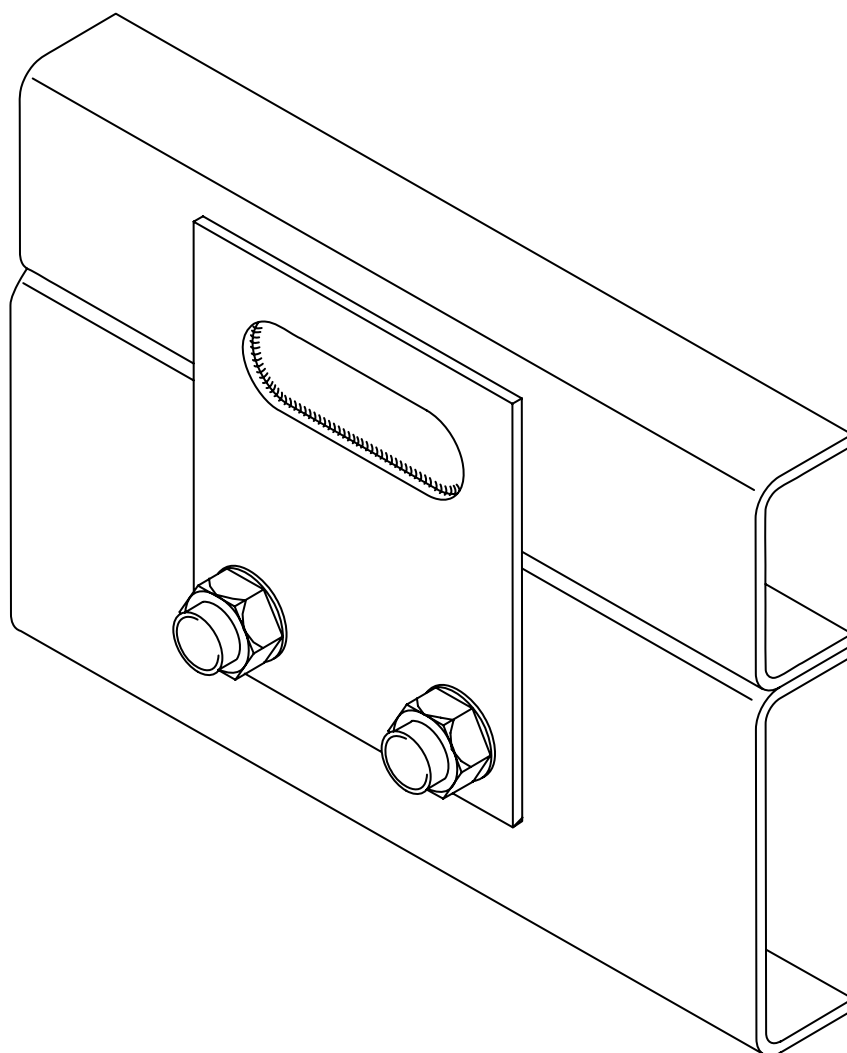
Montagem de chassis auxiliar com rebite de soldadura ESC-025
